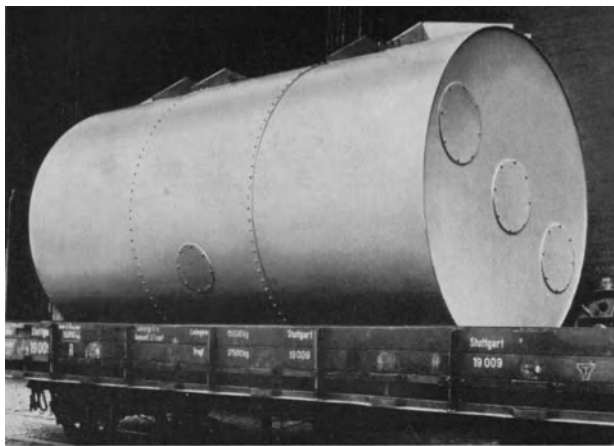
Elektrisch geschweißter Gegengewichtsbehälter für einen Buckauer Doppeltor-Schwenkbagger, 625 l Eimerinhalt. Inhalt des Behälters 70 bis 80 t.
